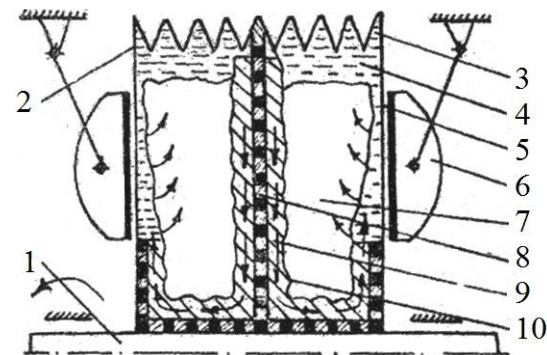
Охолоджуючий пристрій, вбудований в гальмівний диск, який обертається на валу: 1 - вал; 2, 3 - герметичний корпус диска і його торцеві поверхні; 4 - гальмівні колодки; 5, 6 - зони: випаровування, конденсації; 7 - капілярно-пористий вкладиш; 8 - теплоносій; 9 - феромагнітна оболонка механічної хвилі, що біжить; 10 – індуктор з електромагнітним полем, що біжить
